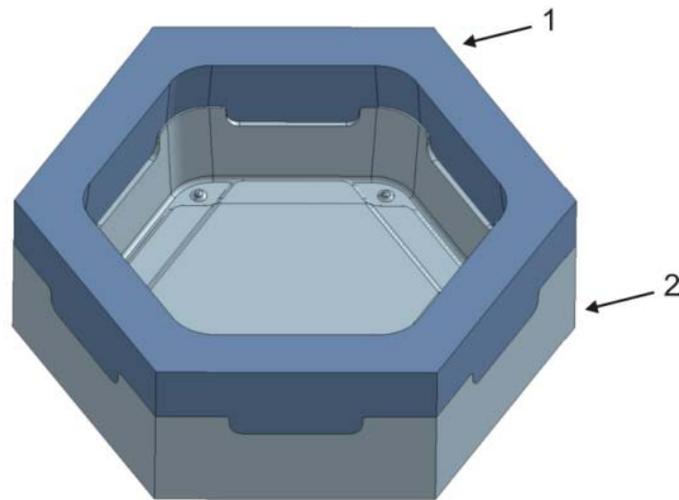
29: Molde de gesso completo, contendo as duas partes.
